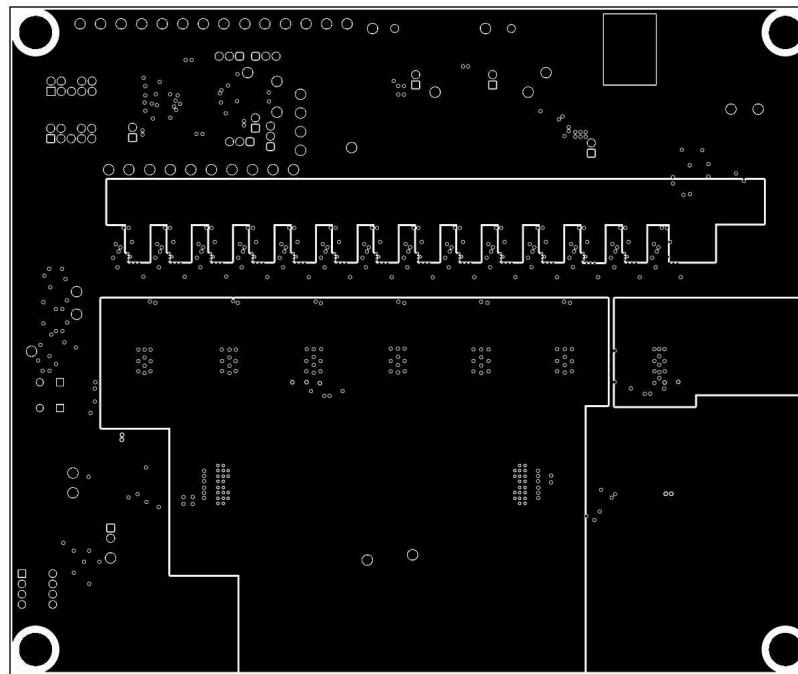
TPS53676EVM-084 PCB 第 5 层 - 电源
